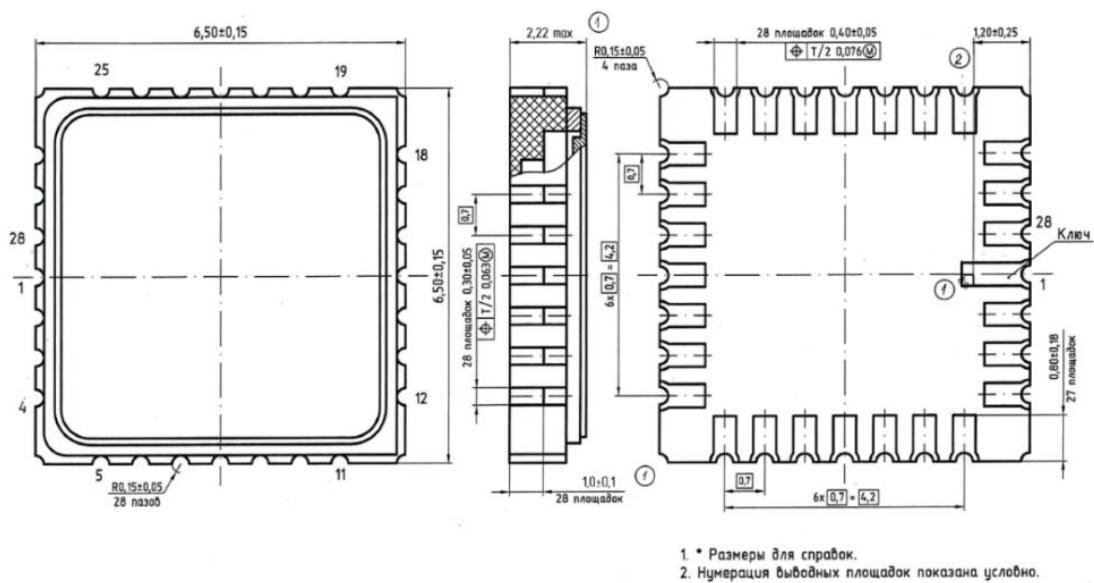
Габаритный чертеж корпуса 5123.28-1.01 (размеры в мм)
